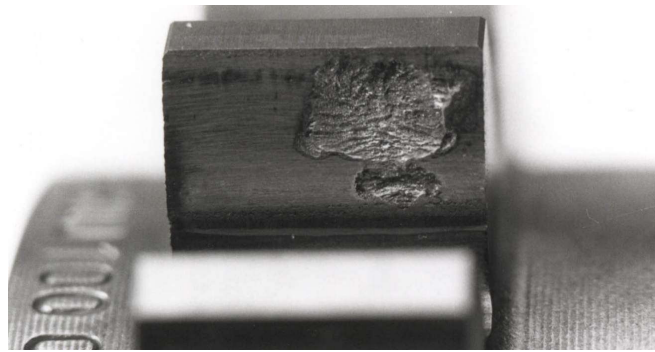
Pată de uzare prin pitting a flancului [W20]
